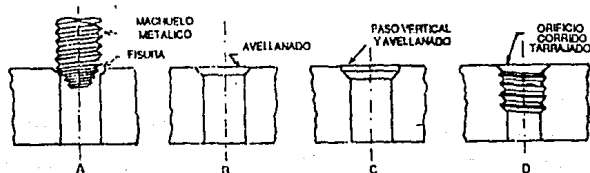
Abocardado recomendado para rocas machueladas. (Ref. 2).
